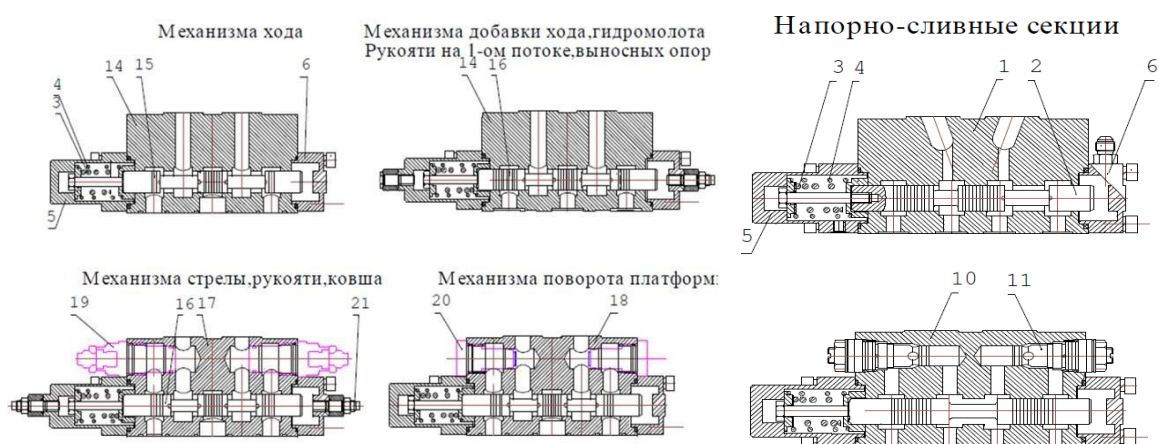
Конструкция секции гидрораспределителя: 1, 14, 17, 18 – корпус; 2, 15, 16 – золотники; 3, 4 – пружины; 5, 6 – крышки; 10, 11 – предохранительные клапаны; 19 – предохранительно - подпиточный клапан; 20 – подпиточный клапан; 21 – ограничитель хода золотника.
